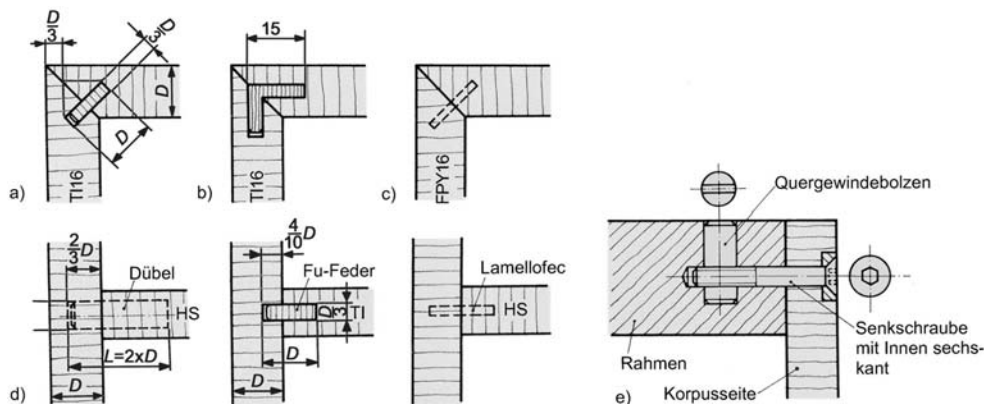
Gedübelte Korpuseckverbindungen (Schnitte) a) auf Gehrung gedübelt, b) stumpf gedübelt
